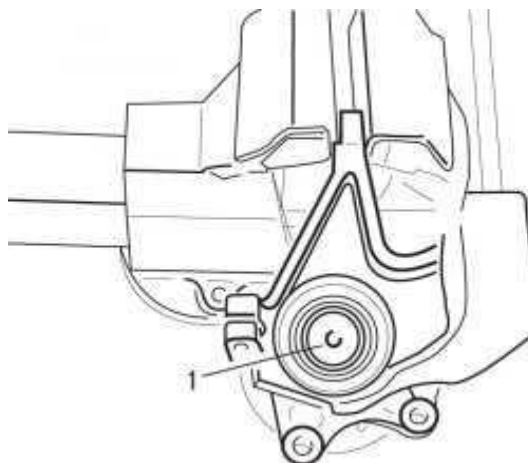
Установка натискного вкладиша “0621-Е” для видавлювання маточини з поворотної цапфи: 1 – пристосування “0621-Е”
